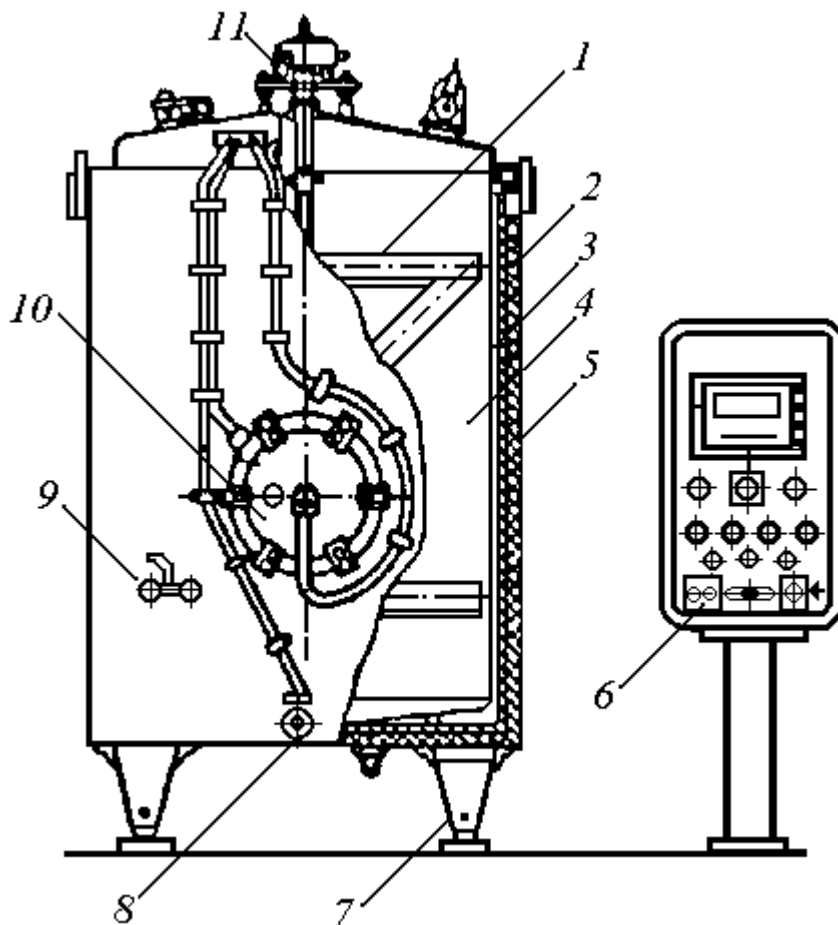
Резервуар для приготовления кисломолочных продуктов:
